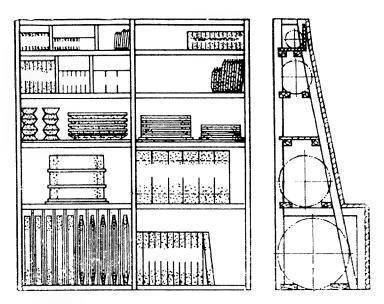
Схема хранения шлифовальных кругов на стеллажах
